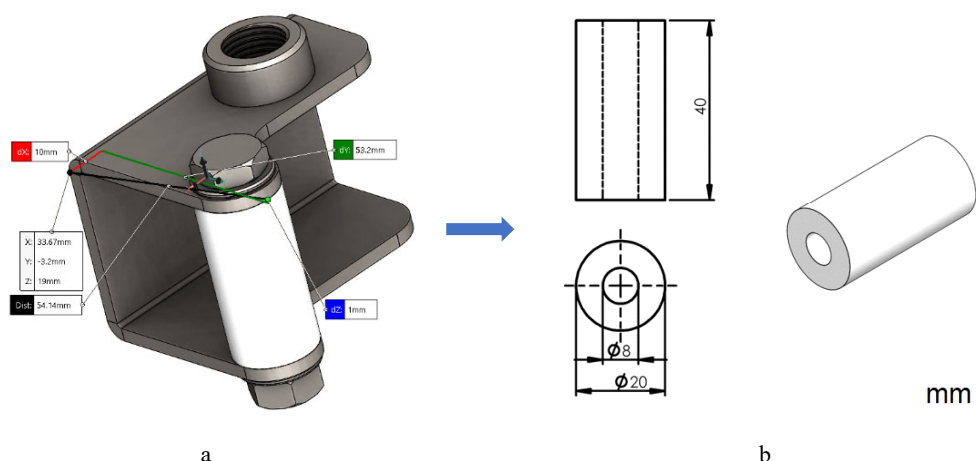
a) Conjunto vínculo; b) rodillo deslizante.
